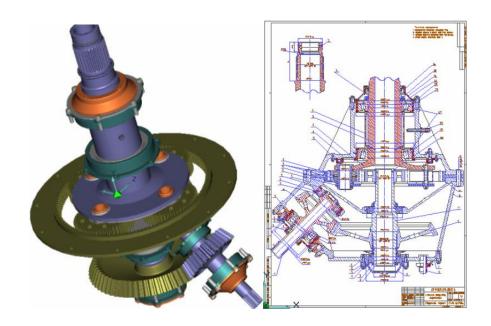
3D сборка и сборочный чертеж редуктора
